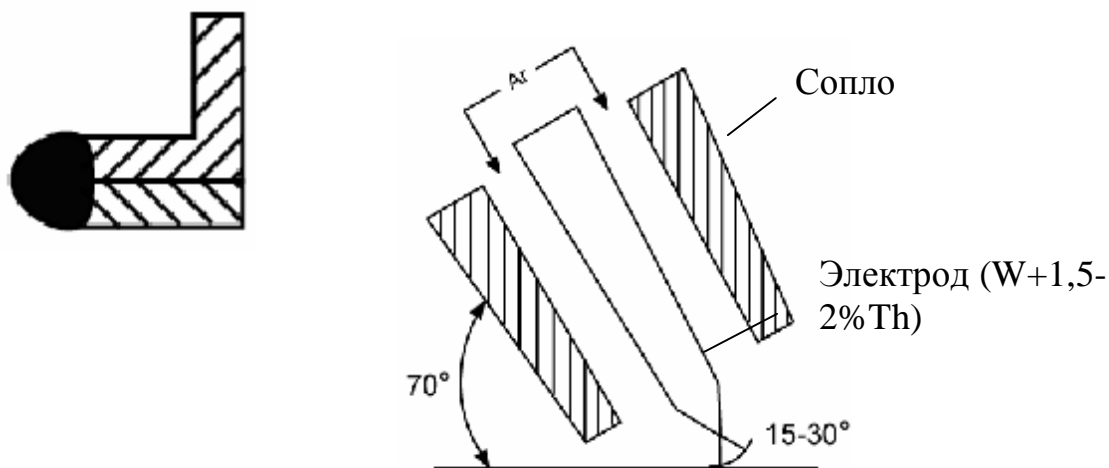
Схема аргонно-дуговой сварки и вид сварного шва
